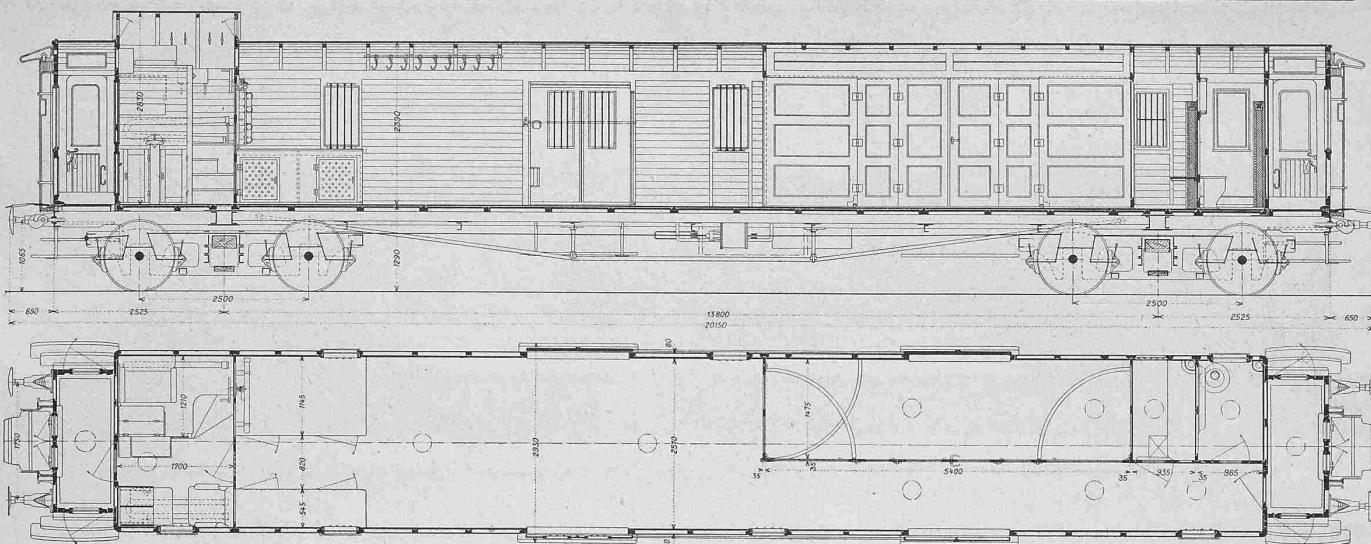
Gepäckwagen F 4ü der Lötschbergbahn, gebaut von der Wagons-Fabrik Schlieren (W. F. S.). — Längs- und Horizontalschnitt. — 1:100.
